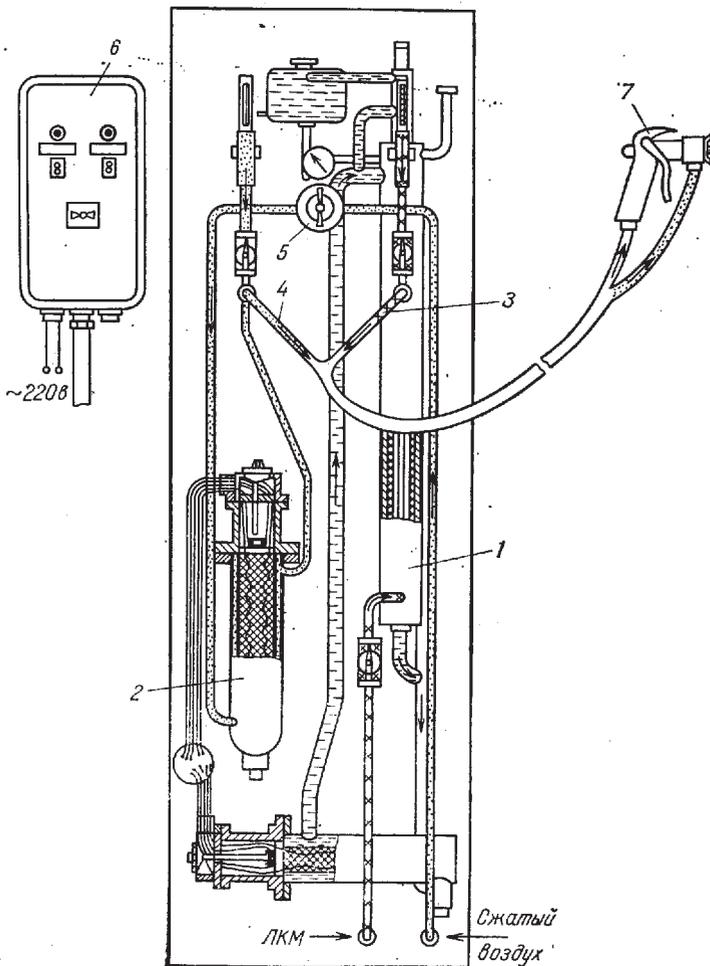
Стационарная установка УГО-5М для нанесения нагретых ЛКМ: 1 — нагреватель ЛКМ; 2 — воздухонагреватель; 3 — краскоподающий шланг; 4 — воздушный шланг; 5 — регулятор давления; 6 — выносной пульт управления; 7 — краскораспылитель
